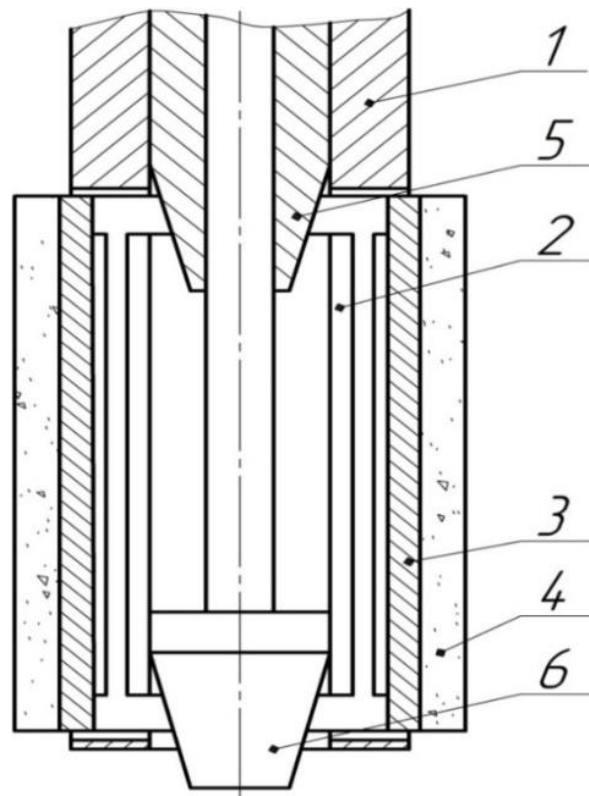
Елементи конструкції хонінгувальної головки, яка реалізує новий спосіб хонінгування: 1 – корпус; 2 – конусні планки; 3 – колодки; 4 – абразивні бруски; 5 – верхній розтискний конус; 6 – нижній розтискний конус
